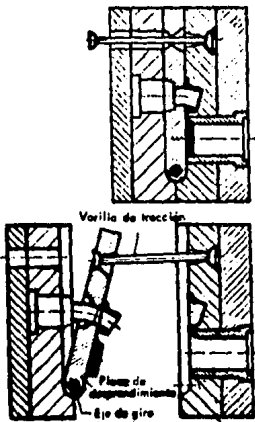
Desprendimiento mediante una placa de molde basculante.
